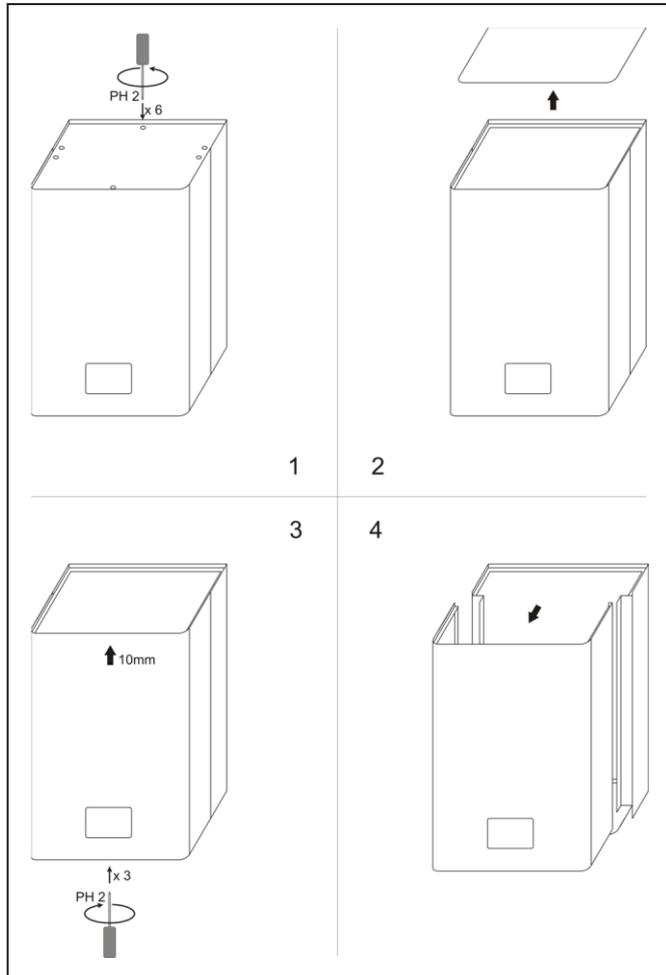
Ouverture de la chaudière (démontage du capot avant)
